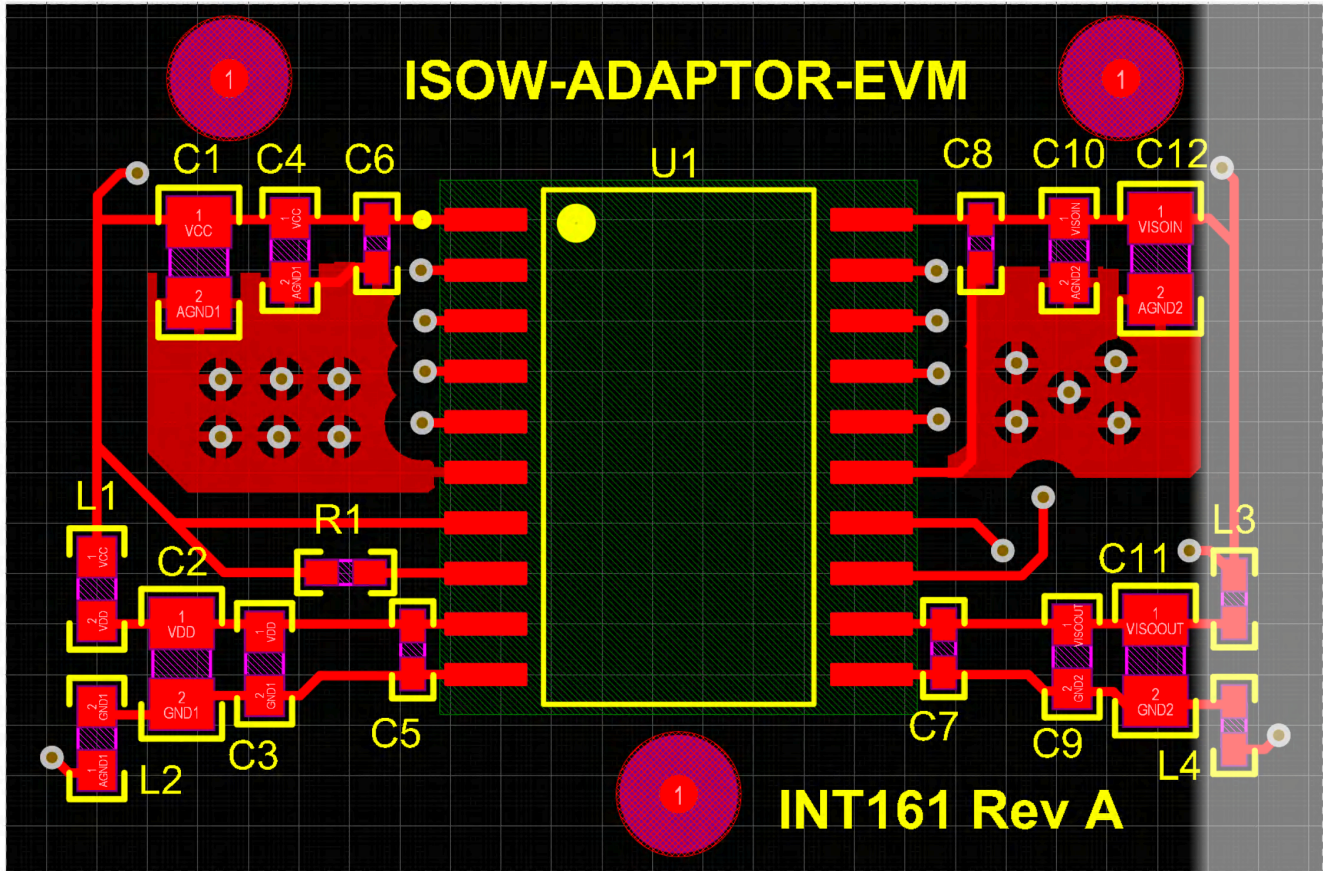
ISOW-ADAPTOR-EVM PCB 布局 - 顶层
